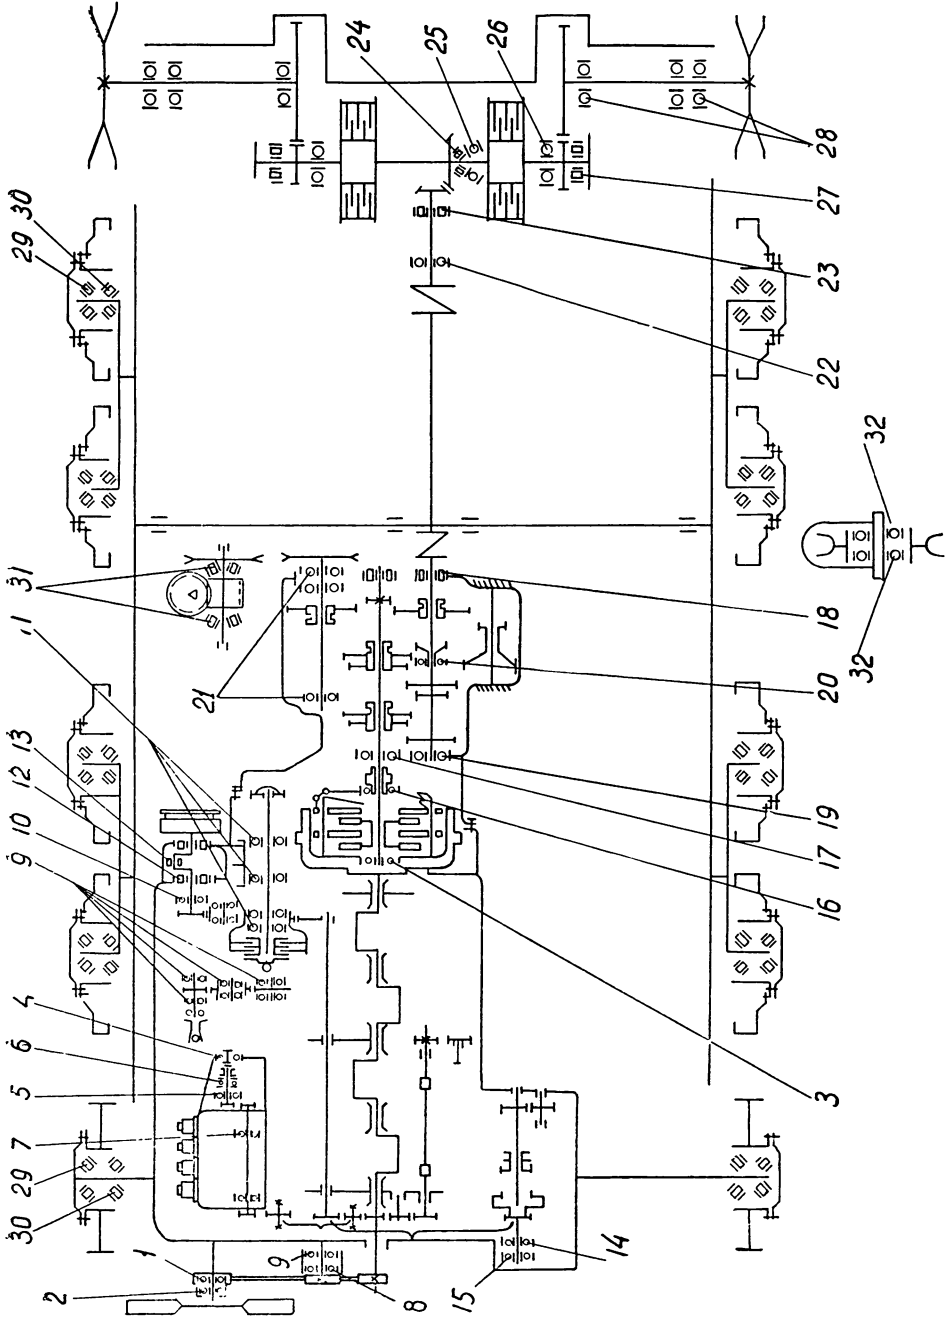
Места установки подшипников качения трактора ТДТ-40М
